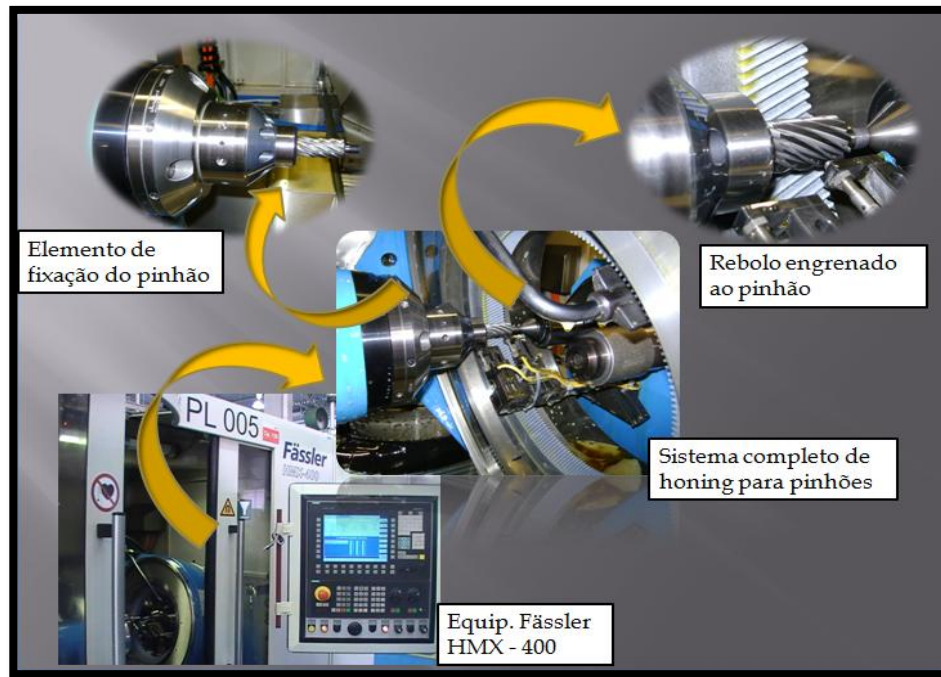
Detalhe do cabeçote de usinagem, HMX-400 (Fässler, 2008).
